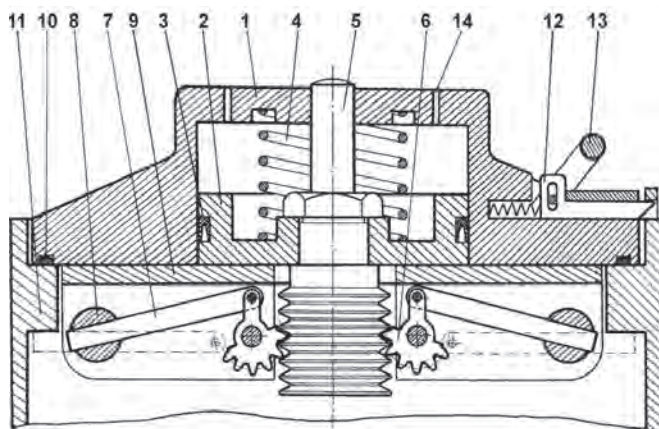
Схема конструкции быстросъемной крышки сосуда высокого давления
